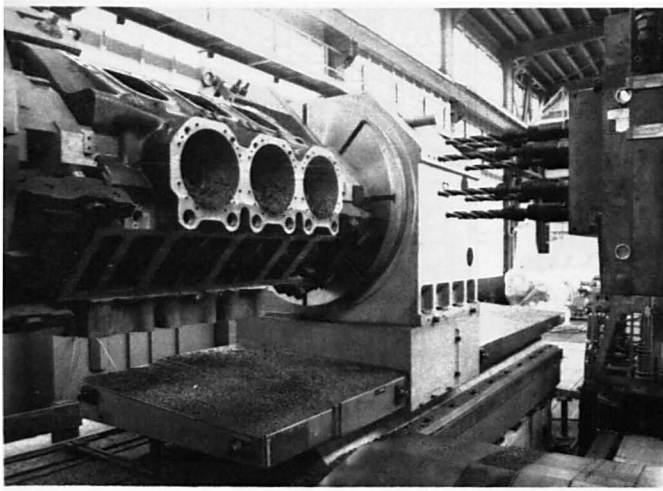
Bearbeitung eines 6-Zylinder-Kurbelgehäuses im Wendespanner mit Mehrspindel-Bohrkopf («Werner TC 2 So»)
